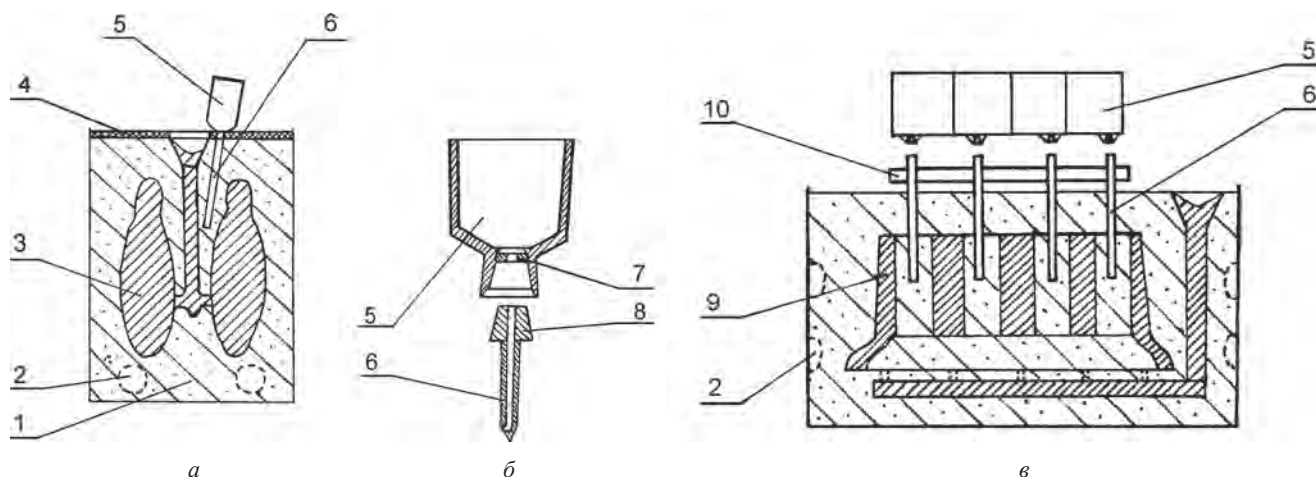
Вакуулируемые формы с дозаторами воды: контейнерная форма с дозатором воды (а); разборная емкость-дозатор (б); форма с отливкой типа блока цилиндров (в): 1 – песок; 2 – фильтры; 3 – отливка; 4 – пленка; 5 – емкость-дозатор; 6 – трубчатый штырь; 7 – дозирующая шайба; 8 – конусная пробка; 9 – отливка блока цилиндров; 10 – планка
